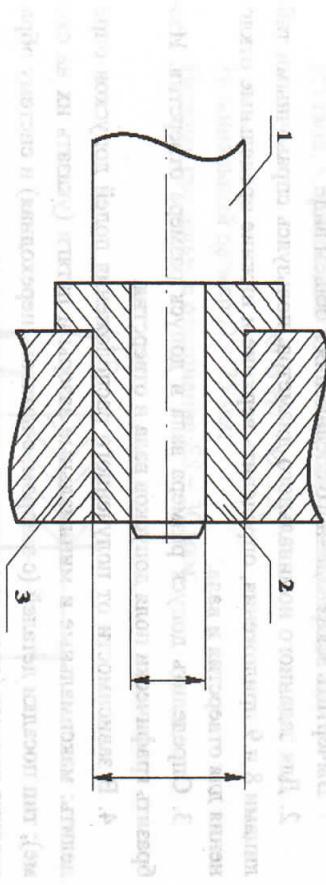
Схема соединения: 1 – вал; 2 – вкладыш подшипника; 3 – корпус.
